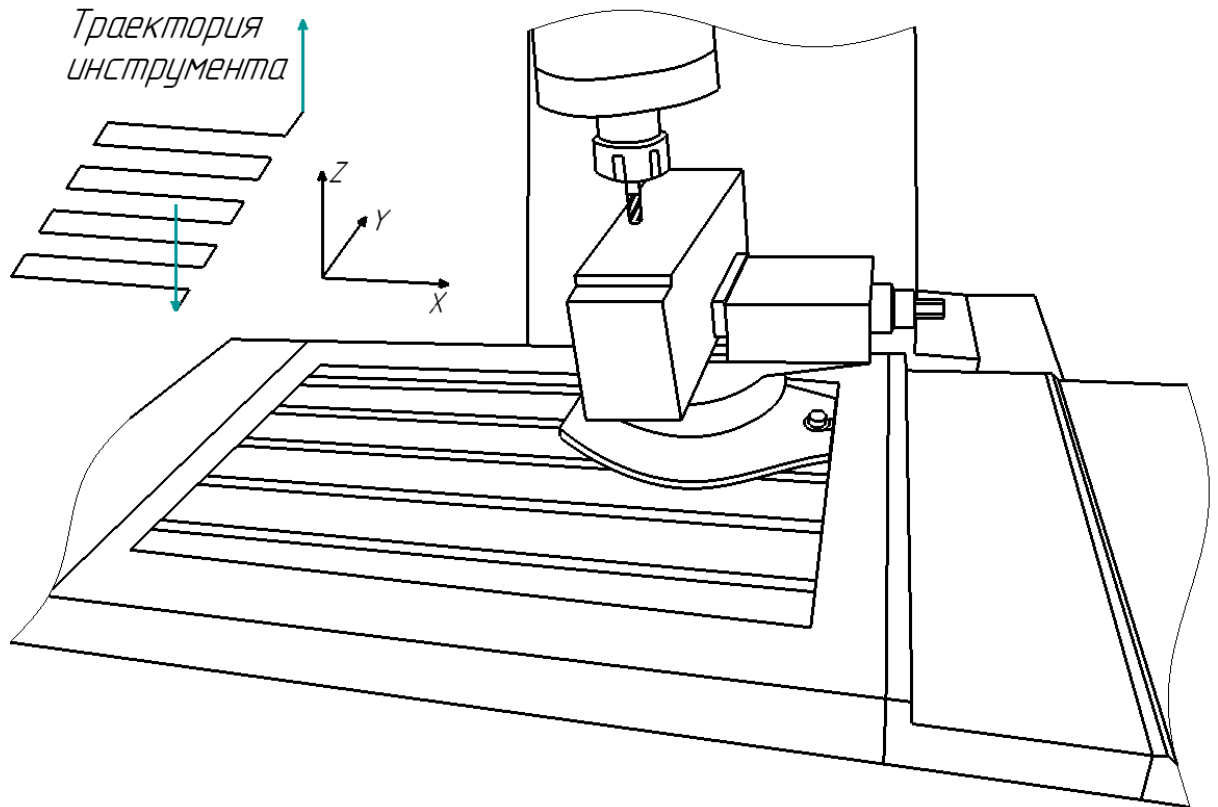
Система станок-приспособление-заготовка-инструмент и траектория перемещения при фрезеровании уступа
